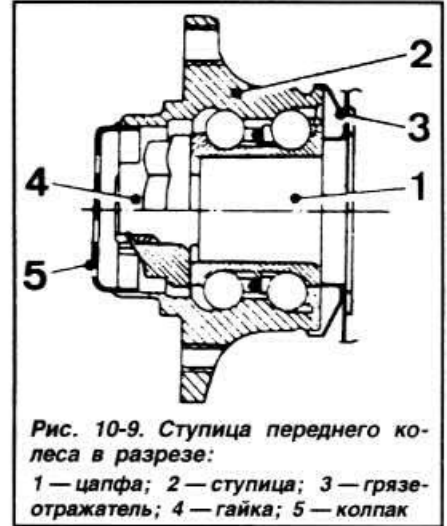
Ступица переднего колеса в разрезе: 1 — цапфа; 2 — ступица; 3 — грязеотражатель; 4 — гайка; 5 — колпак
